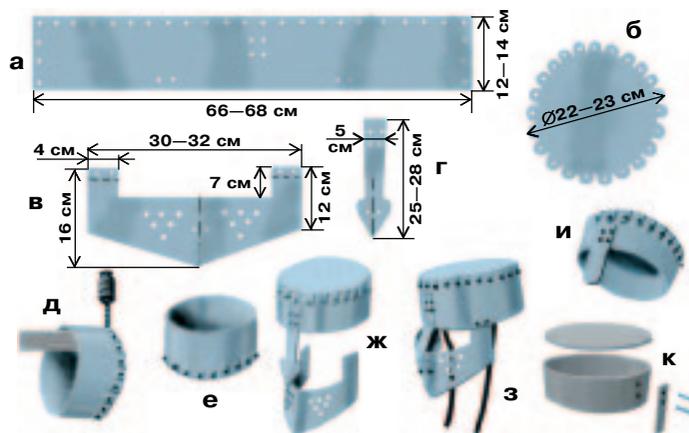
Основные размеры и детали шлема-таблетки: а — тулья; б — крышка; в — полумаска; г — наносник; д — сверление отверстий под заклепки; е — присоединение крышки шлема; ж — присоединение наносника и полумаски; з — завязки из кожаных ремешков; и — простейший шлем-таблетка без полумаски; к — изготовление шлема-таблетки из листового полистирола.
